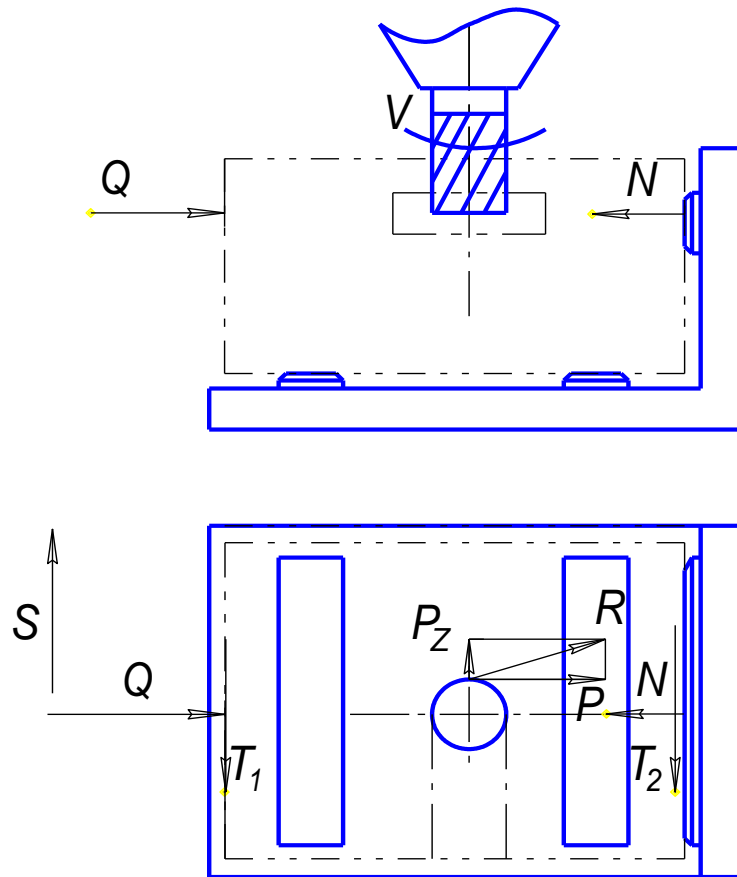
Схема встановлення і закріплення заготовки при фрезеруванні паза
